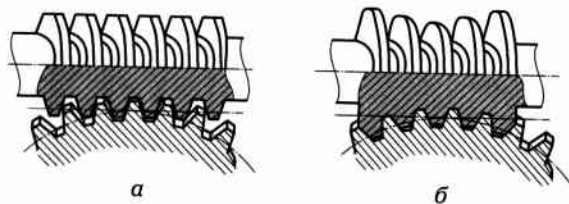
Цилиндрический (а) и глобидный (б) червяки червячной передачи
